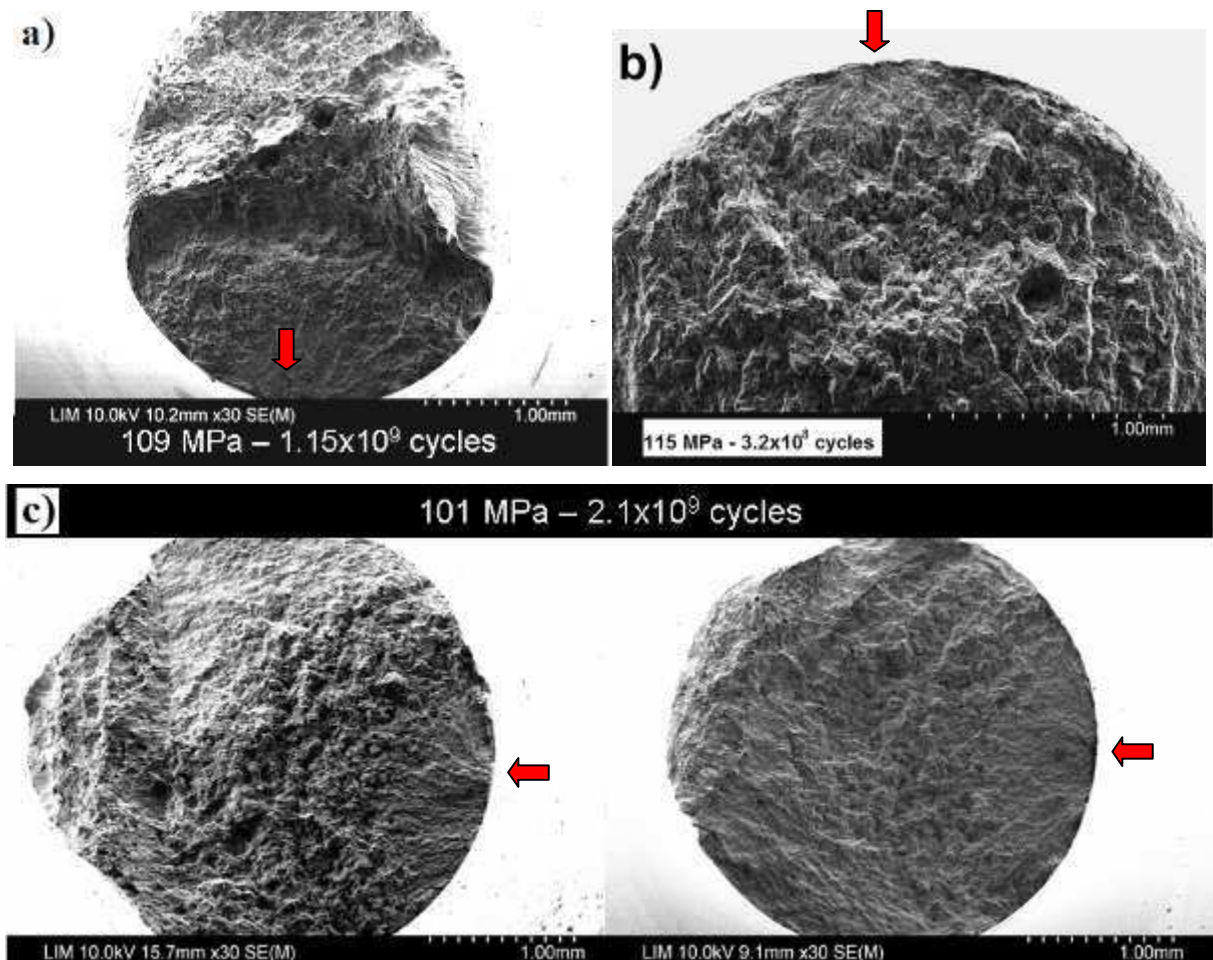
Faciès de rupture des éprouvettes cylindriques sollicitées à 20 KHz par la machine de fatigue ultrasonique - La fissure part de la surface.
